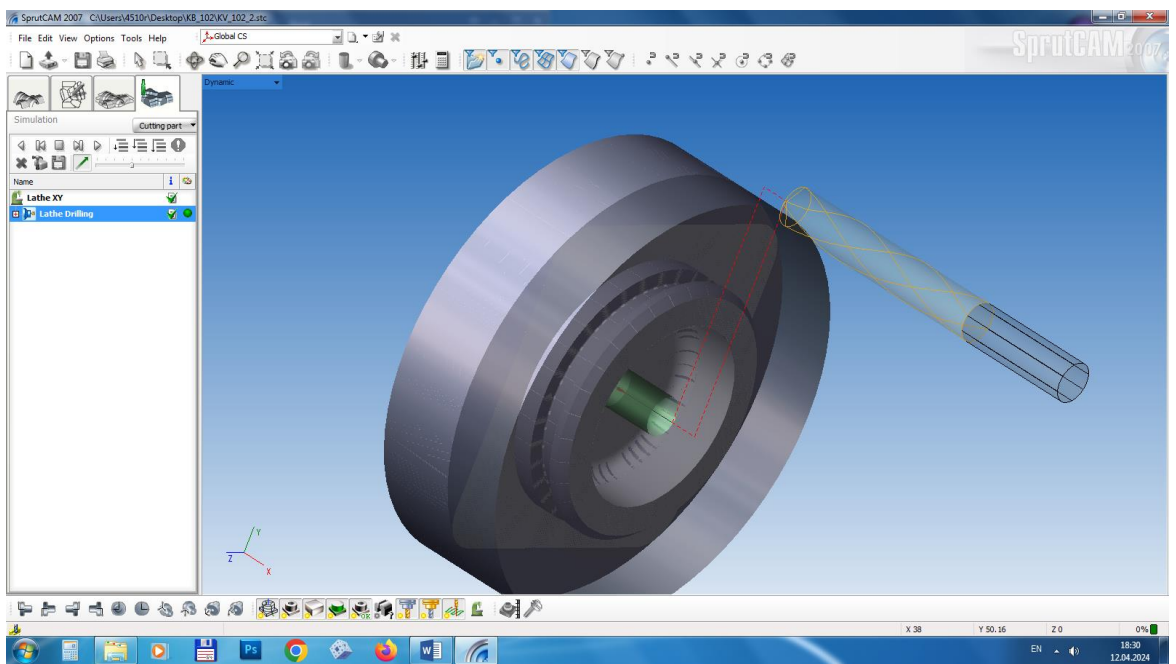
Інструмент і деталь перед свердлінням
